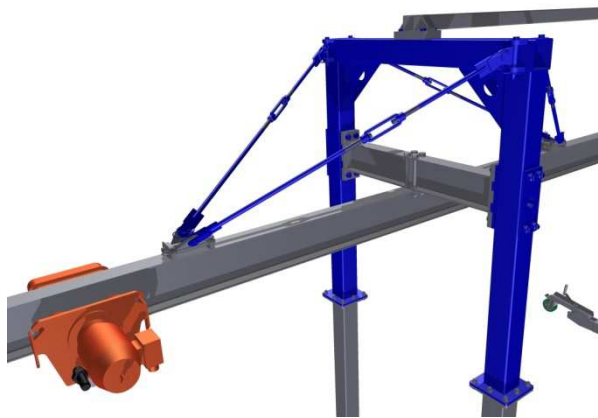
ISO pohled - spodní díl portálu (modře zvýrazněný) s manipulačním podvozkem
